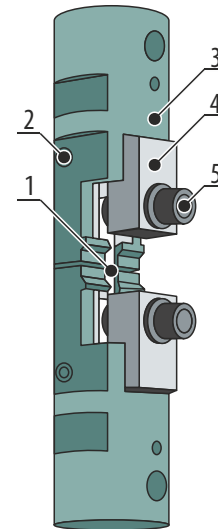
Конструкция устройства для испытаний сегментного образца: 1 — сегментный образец; 2 — стержень; 3 — обойма; 4 — вкладыш; 5 — винт
